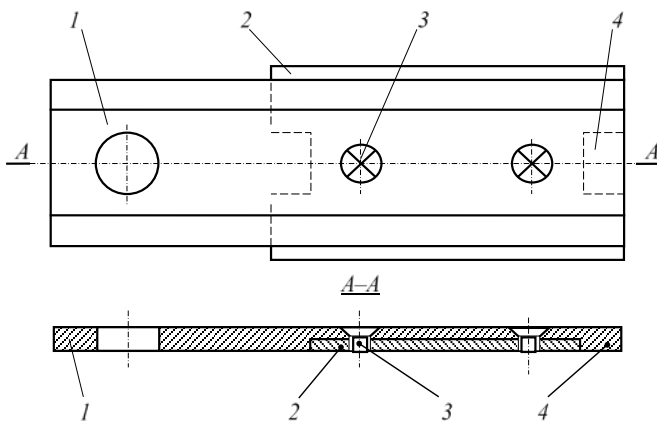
Нож роторной косилки с неподвижной режущей накладкой:
